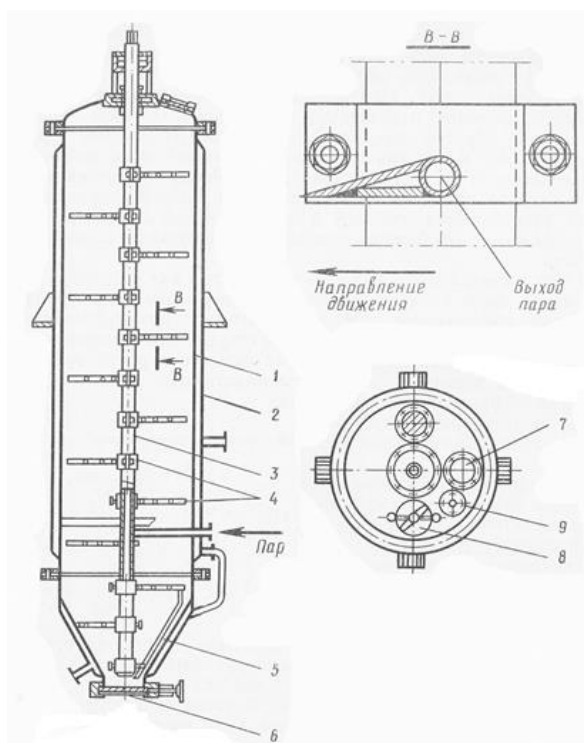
Вертикальний стерилізатор: 1 - корпус; 2 – сорочка; 3 – вал;
